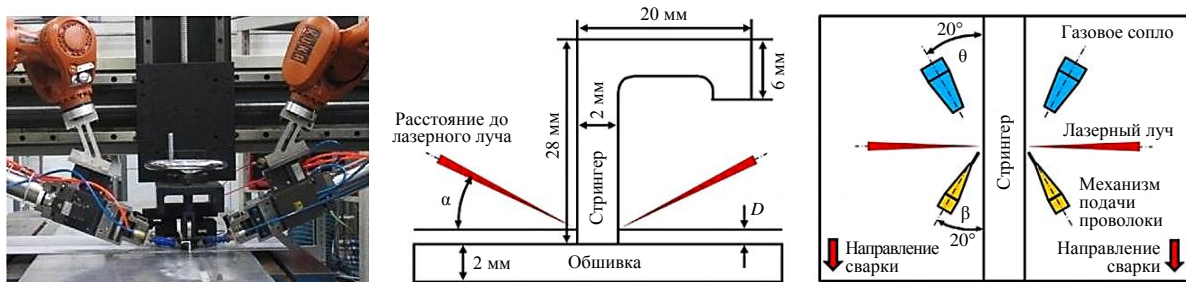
Общий вид и схема процесса двусторонней лазерной сварки [23]
